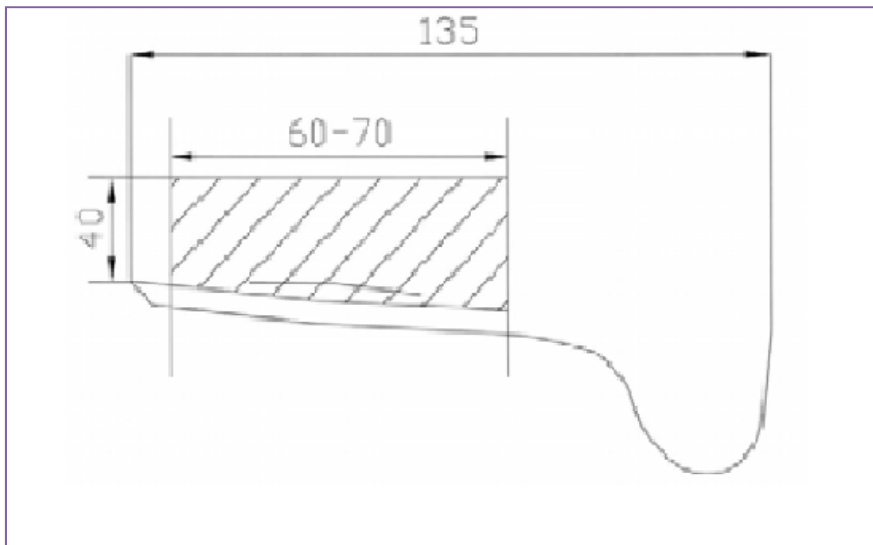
Zona de localización de grietas circunferenciales en la llanta (mm).
